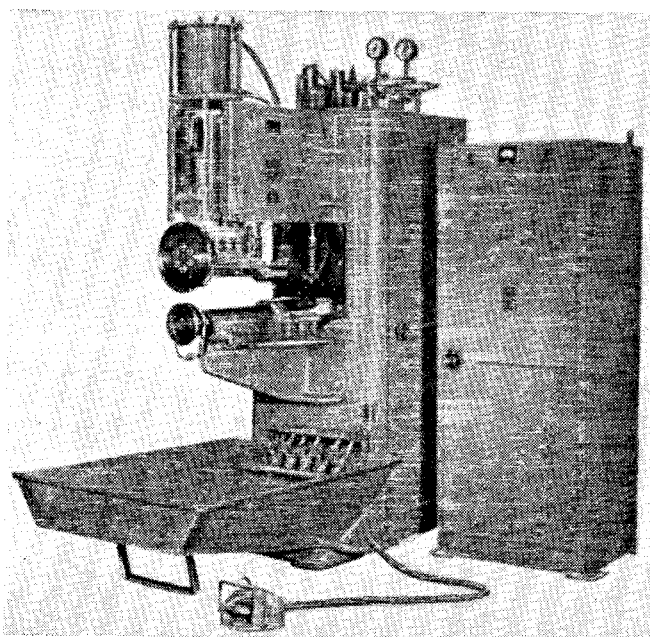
Сварочный агрегат завода „Электрик“. Мощность—150 квв, скорость сварки—до 4 м/мин, толщина свариваемого материала—около 2 мм.
